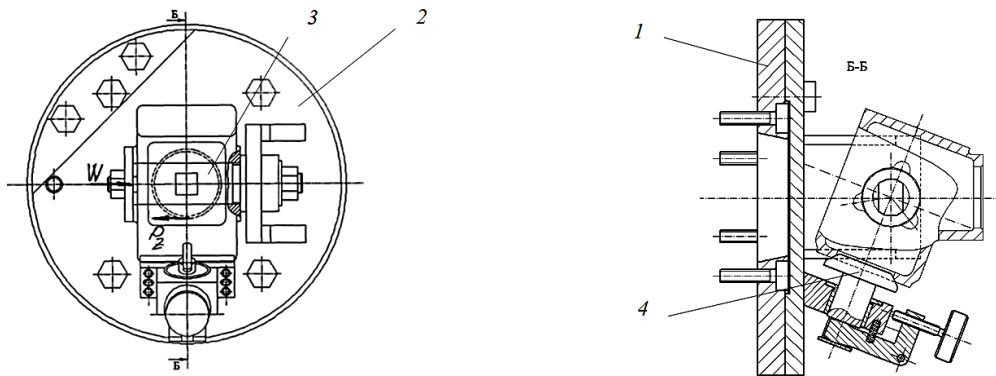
Схема спеціального верстатного пристрою для розточування основного отвору у корпусній заготовці, який має кутове зміщення до горизонтальної площини, з базуванням по двох отворах: 1 – планшайба; 2 – диск; 3 – циліндричний палець; 4 – базовий елемент для кутового орієнтування заготовки
